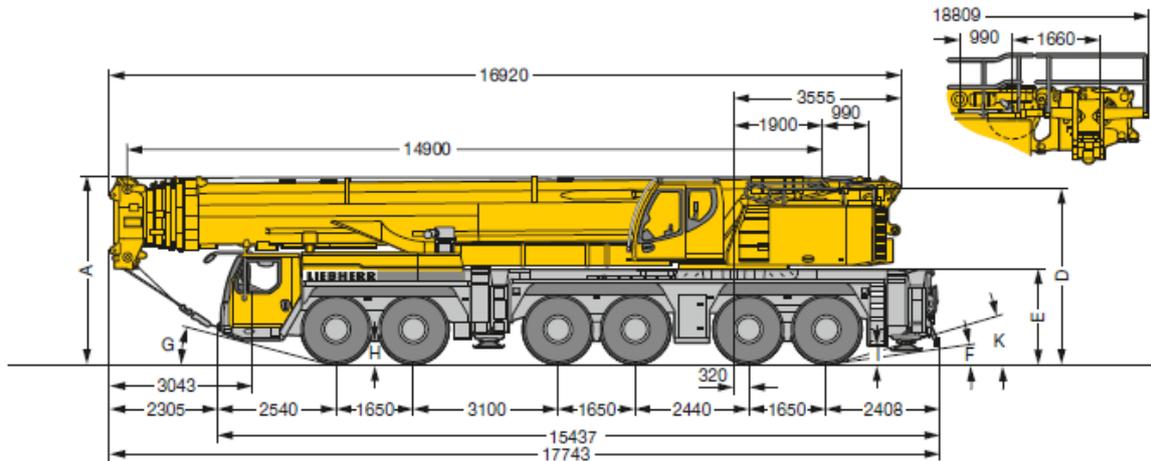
Ansicht 350 t-Mobilkran, hier: Liebherr LTM 1350-6.1
